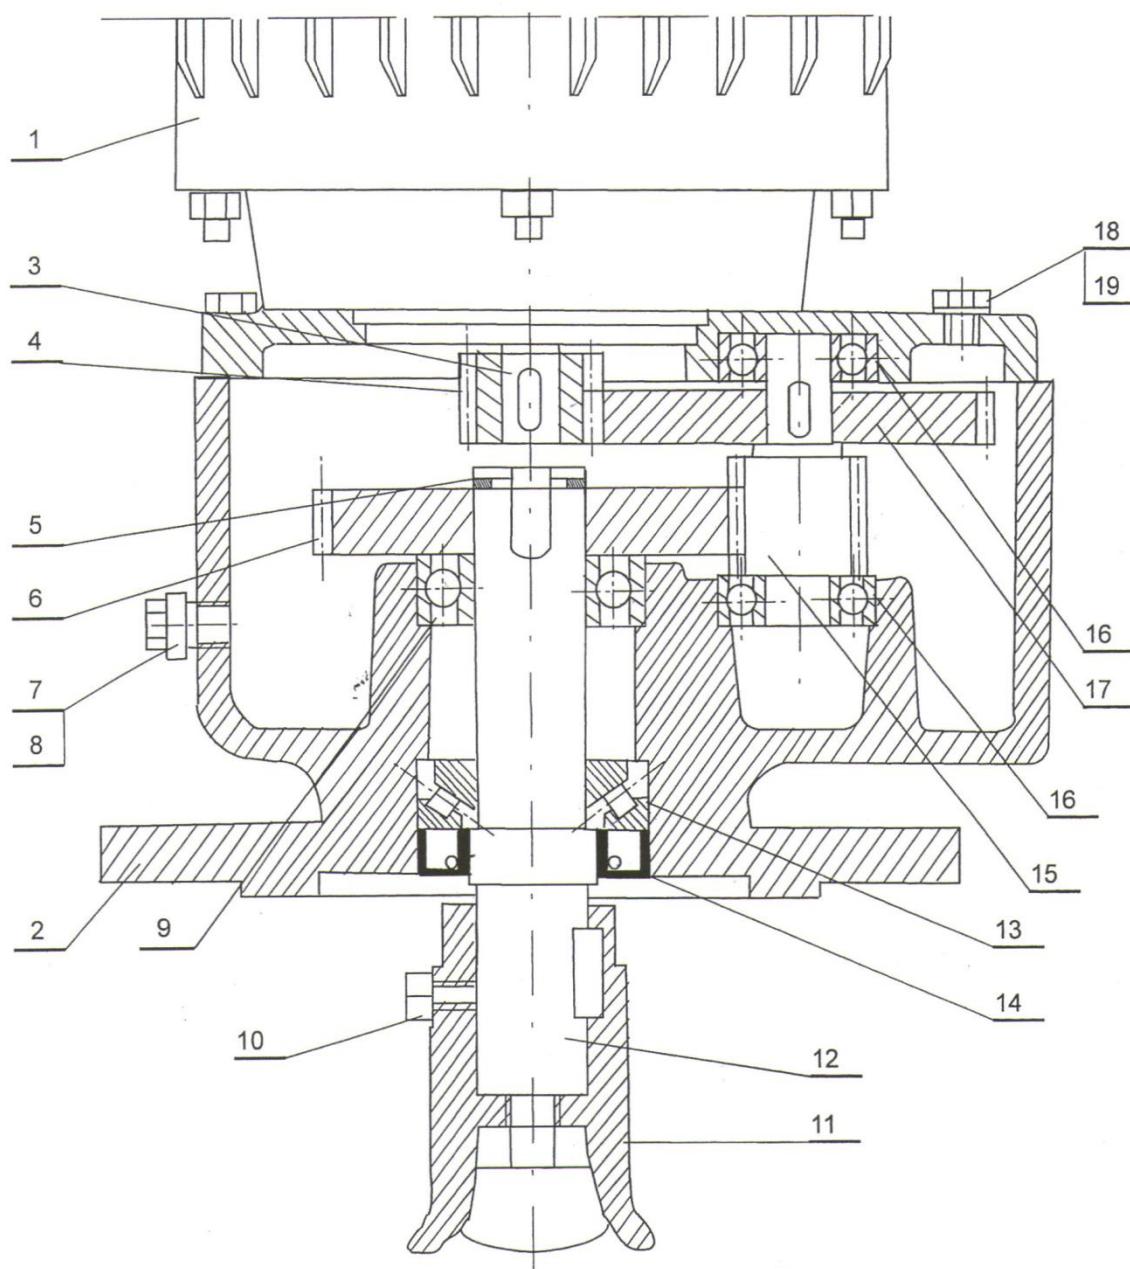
МОТОРЕДУКТОР МЕШАЛКИ И ВИНТОВОГО НАСОСА
